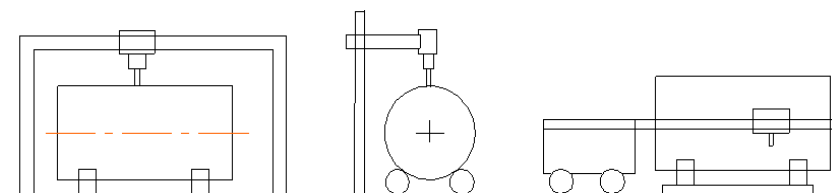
Установки для сварки прямолинейных стыковых швов
